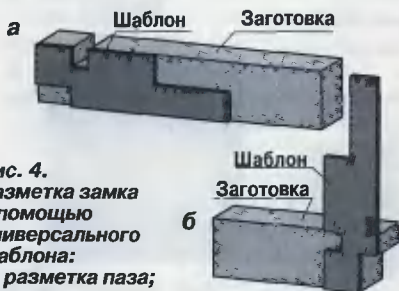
Разметка замка с помощью универсального шаблона: а) разметка паза; б) разметка шипа
